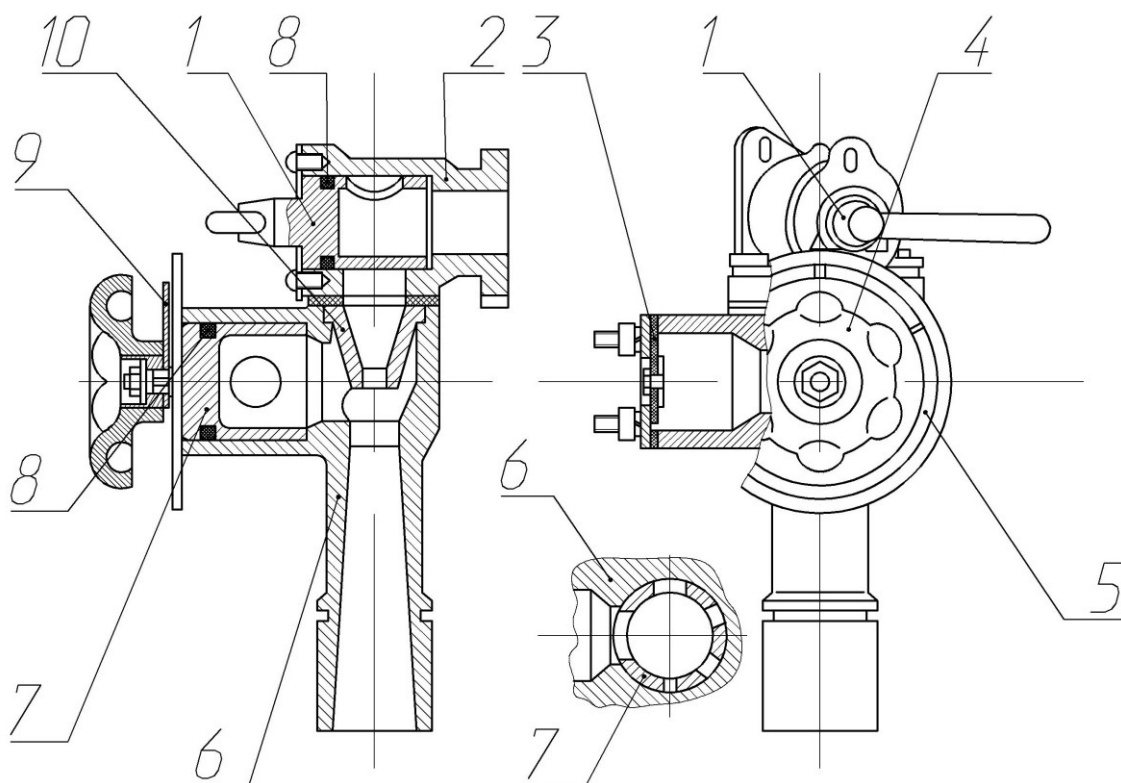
Пеносмеситель ПС-5: 1 – пробка крана пеносмесителя; 2 – корпус крана пеносмесителя; 3 – обратный клапан; 4 – маховичок дозатора (ручка); 5 - шкала; 6 – корпус (диффузор); 7 - дозатор; 8 – кольцо уплотнительное; 9 – стрелка; 10 – сопло.
